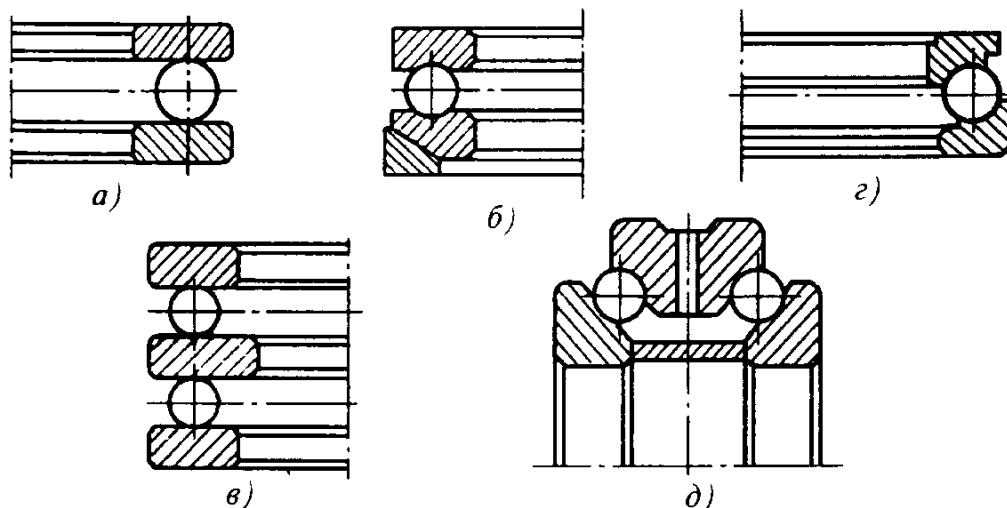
Подшипники упорные и упорно-радиальные шариковые исполнений:
